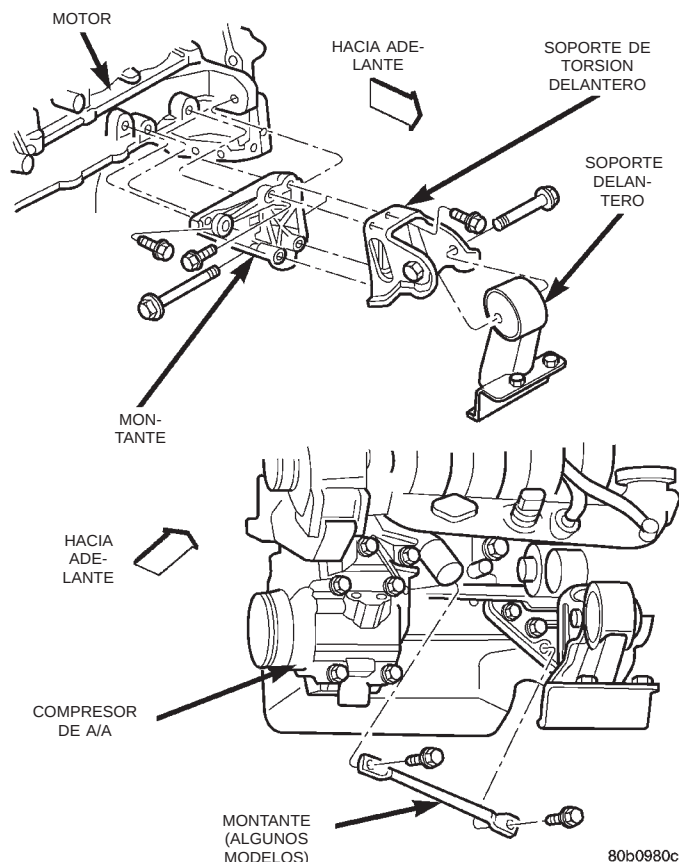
Montaje del motor —Delantero del motor 2.4L
